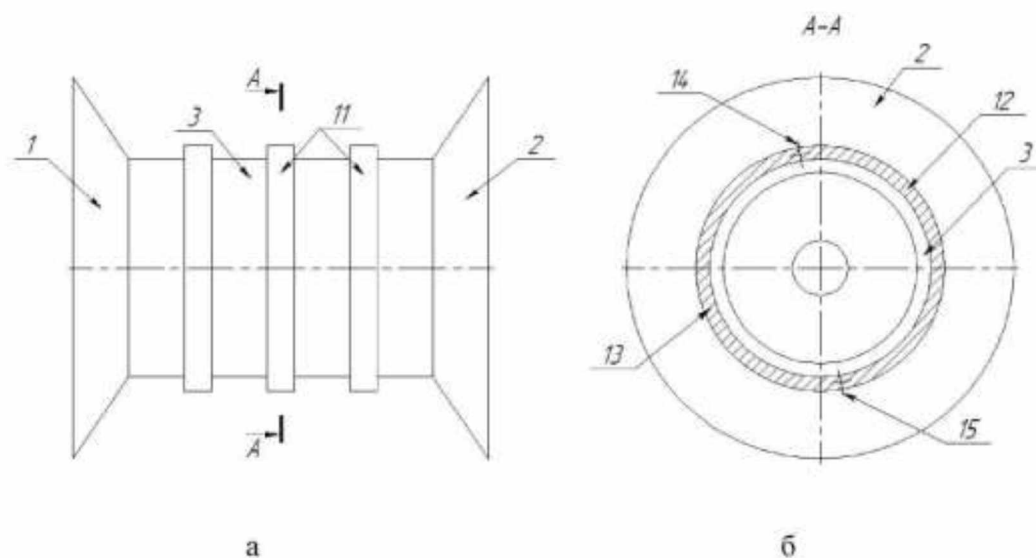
а. Каток опорний картоплезбирального комбайна ККР-2 (модернізований) вид попереду; б - розріз А-А катка опорного [78]
